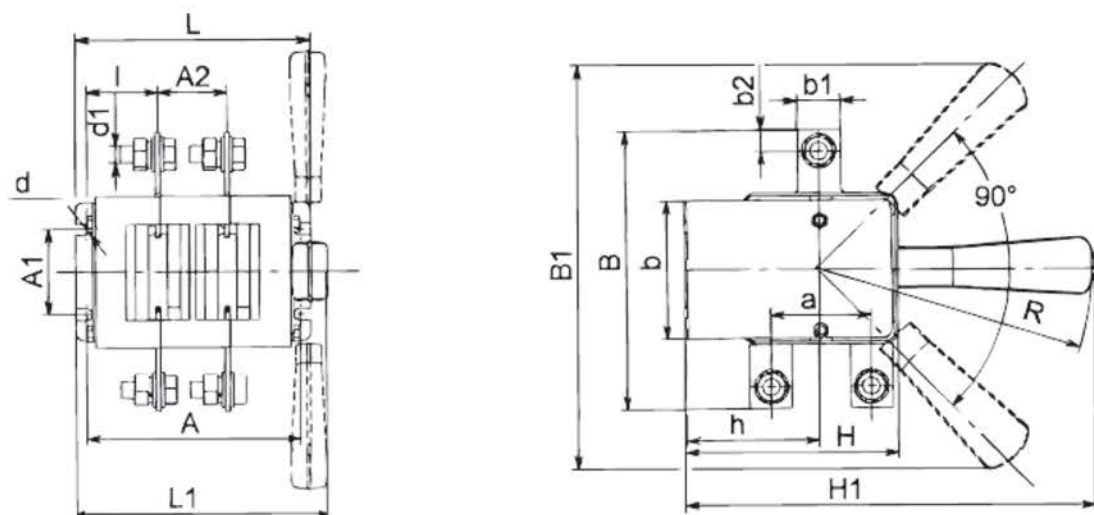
Выключатель-разъединитель двухполюсный на одно направление с боковой смещенной рукояткой.
